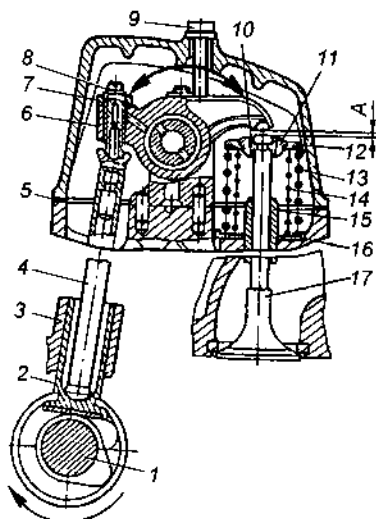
Газораспределительный механизм двигателя КамАЗ-740: *A* — тепловой зазор; 1 — распределительный вал; 2 — толкатель; 3 — направляющая толкателя; 4 — штанга; 5 — прокладка крышки; 6 — коромысло; 7 — гайка; 8 — регулировочный винт; 9 — болт крепления крышки; 10 — сухарь; 11 — втулка тарелки; 12 — тарелка пружины; 13 и 14 — клапанные пружины; 15 — направляющая клапана; 16 — упорная шайба; 17 — клапан
